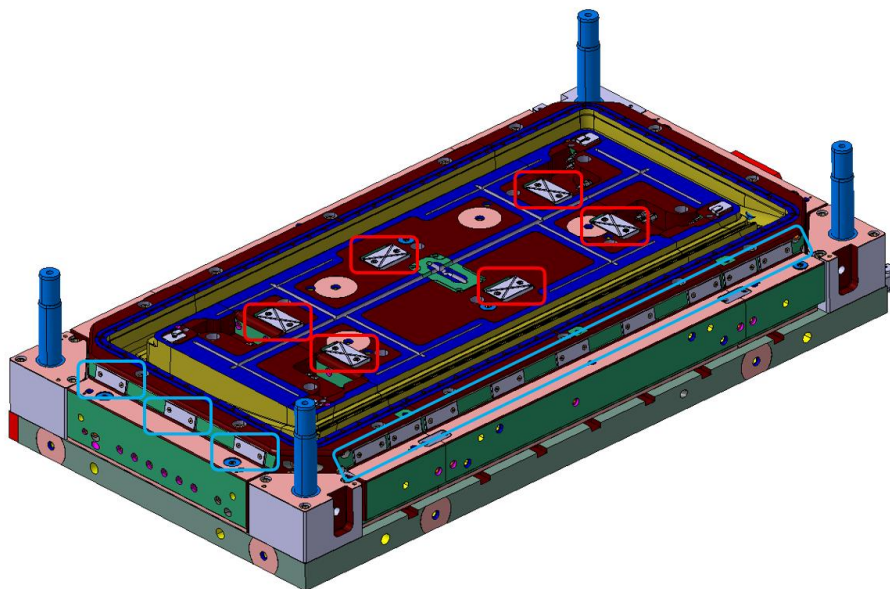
Representação das placas de pressão e das placas de deslize do lado fixo do molde, assinaladas a vermelho e a azul, respetivamente.
